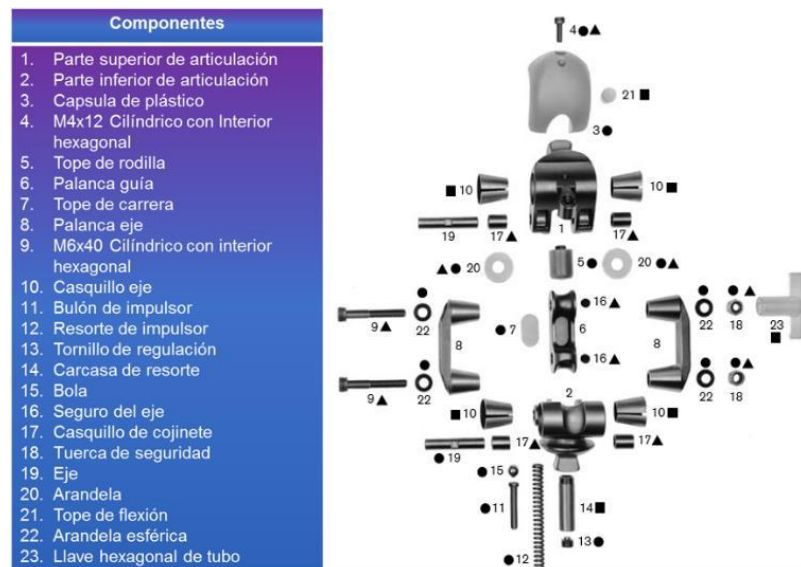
Despiece de la rodilla policéntrica, (OttoBock, 2010)
